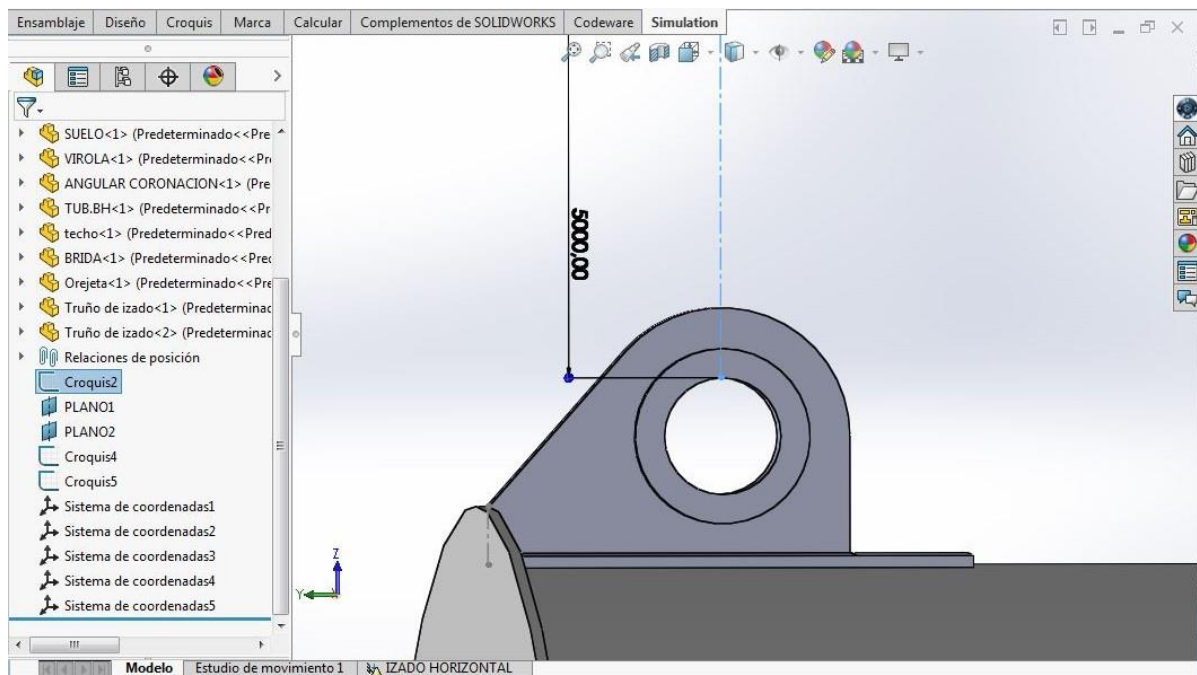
Puntos para sistema de coordenadas de carga remota para izado horizontal del tanque
